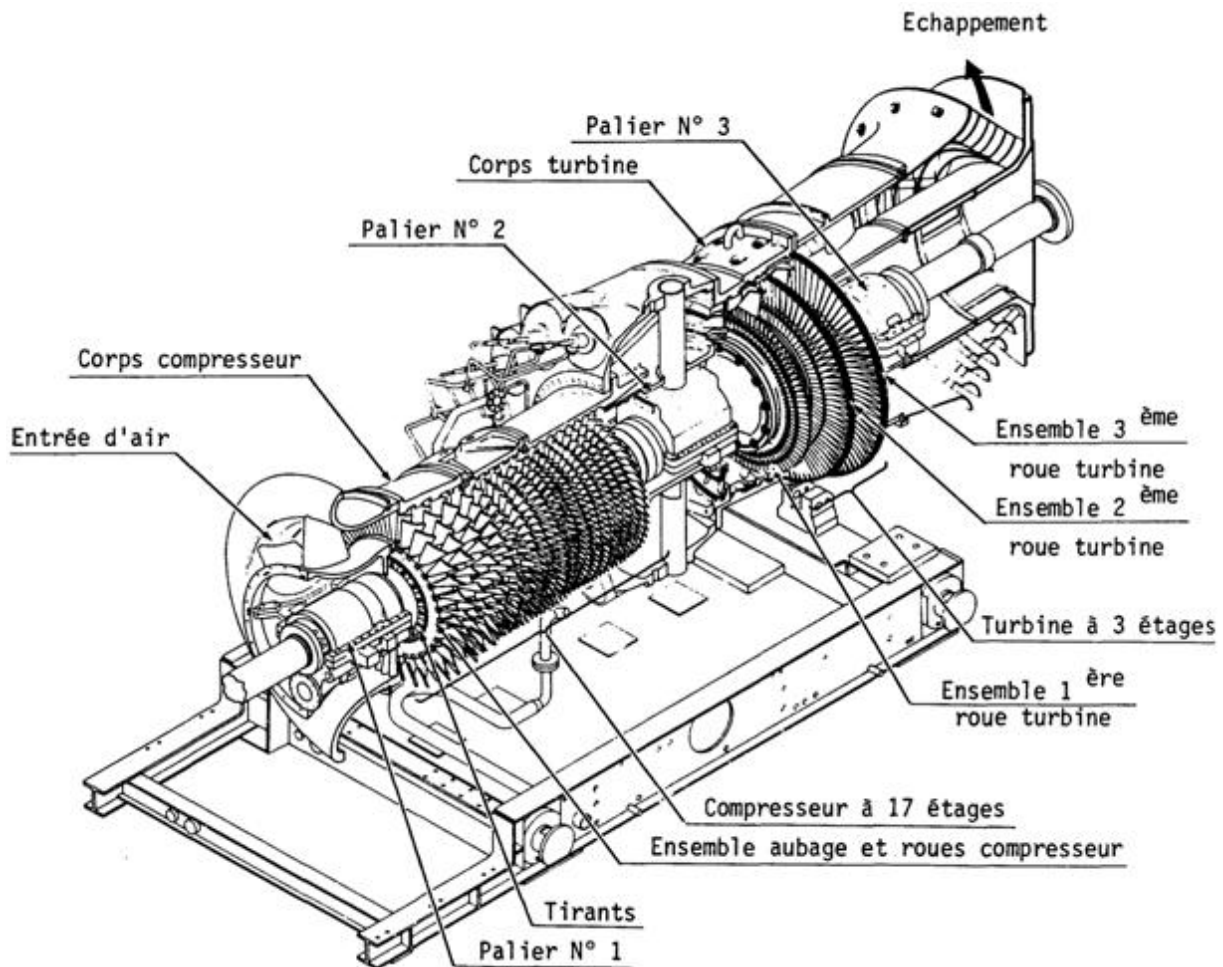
Vue éclatée de la turbine à gaz avec l'ensemble rotor [7].
